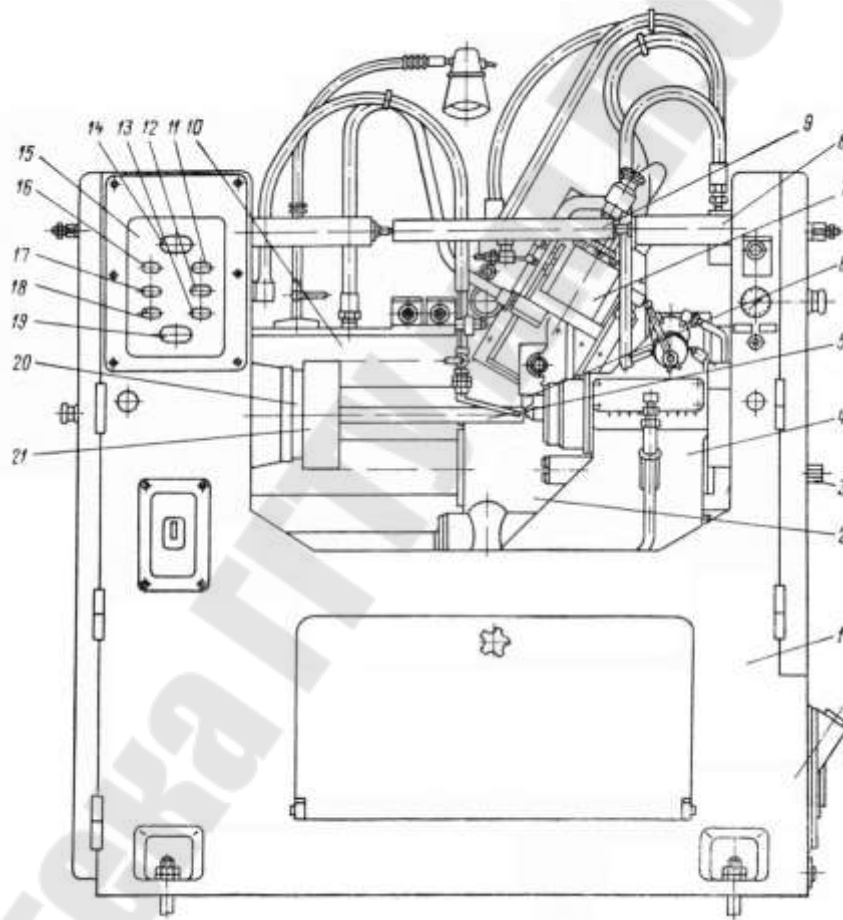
Эскиз общего вида специального токарно-копировального полуавтомата модели СИ-035: 1 – станина; 2 – продольный суппорт; 3 – винт регулировки положения задней бабки; 4 – задняя бабка; 5 – обрабатываемая заготовка; 6 – резец; 7 – копировальный суппорт; 8 – пиноли копира; 9 – копир; 10 – направляющие; 11 – переключатель режимов работы; 12 – кнопка «←»; 13 – кнопка «Цикл»; 14 – лампочка «Напряжение»; 15 – пульт управления; 16 – переключатель охлаждения; 17 – кнопка «→»; 18 – кнопка «Насос»; 19 – кнопка «Стоп»; 20 – шпиндель; 21 – поводковый патрон.
